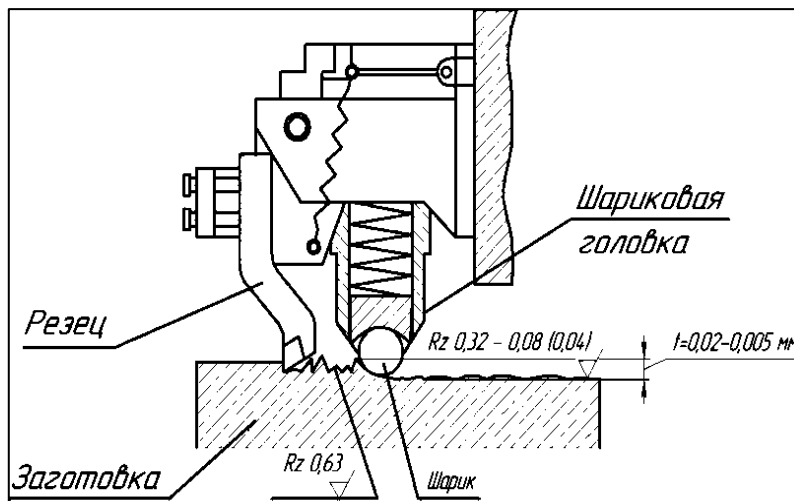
Процесс обработки лезвийными инструментами с последующим накатыванием
